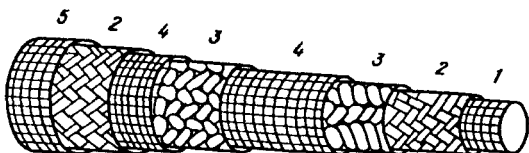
Конструкция рукава высокого давления с металлической оплеткой: 1 – внутренний резиновый слой; 2 – хлопчатобумажная оплетка; 3 – металлическая оплетка; 4 – резиновый слой; 5 – наружный резиновый слой
